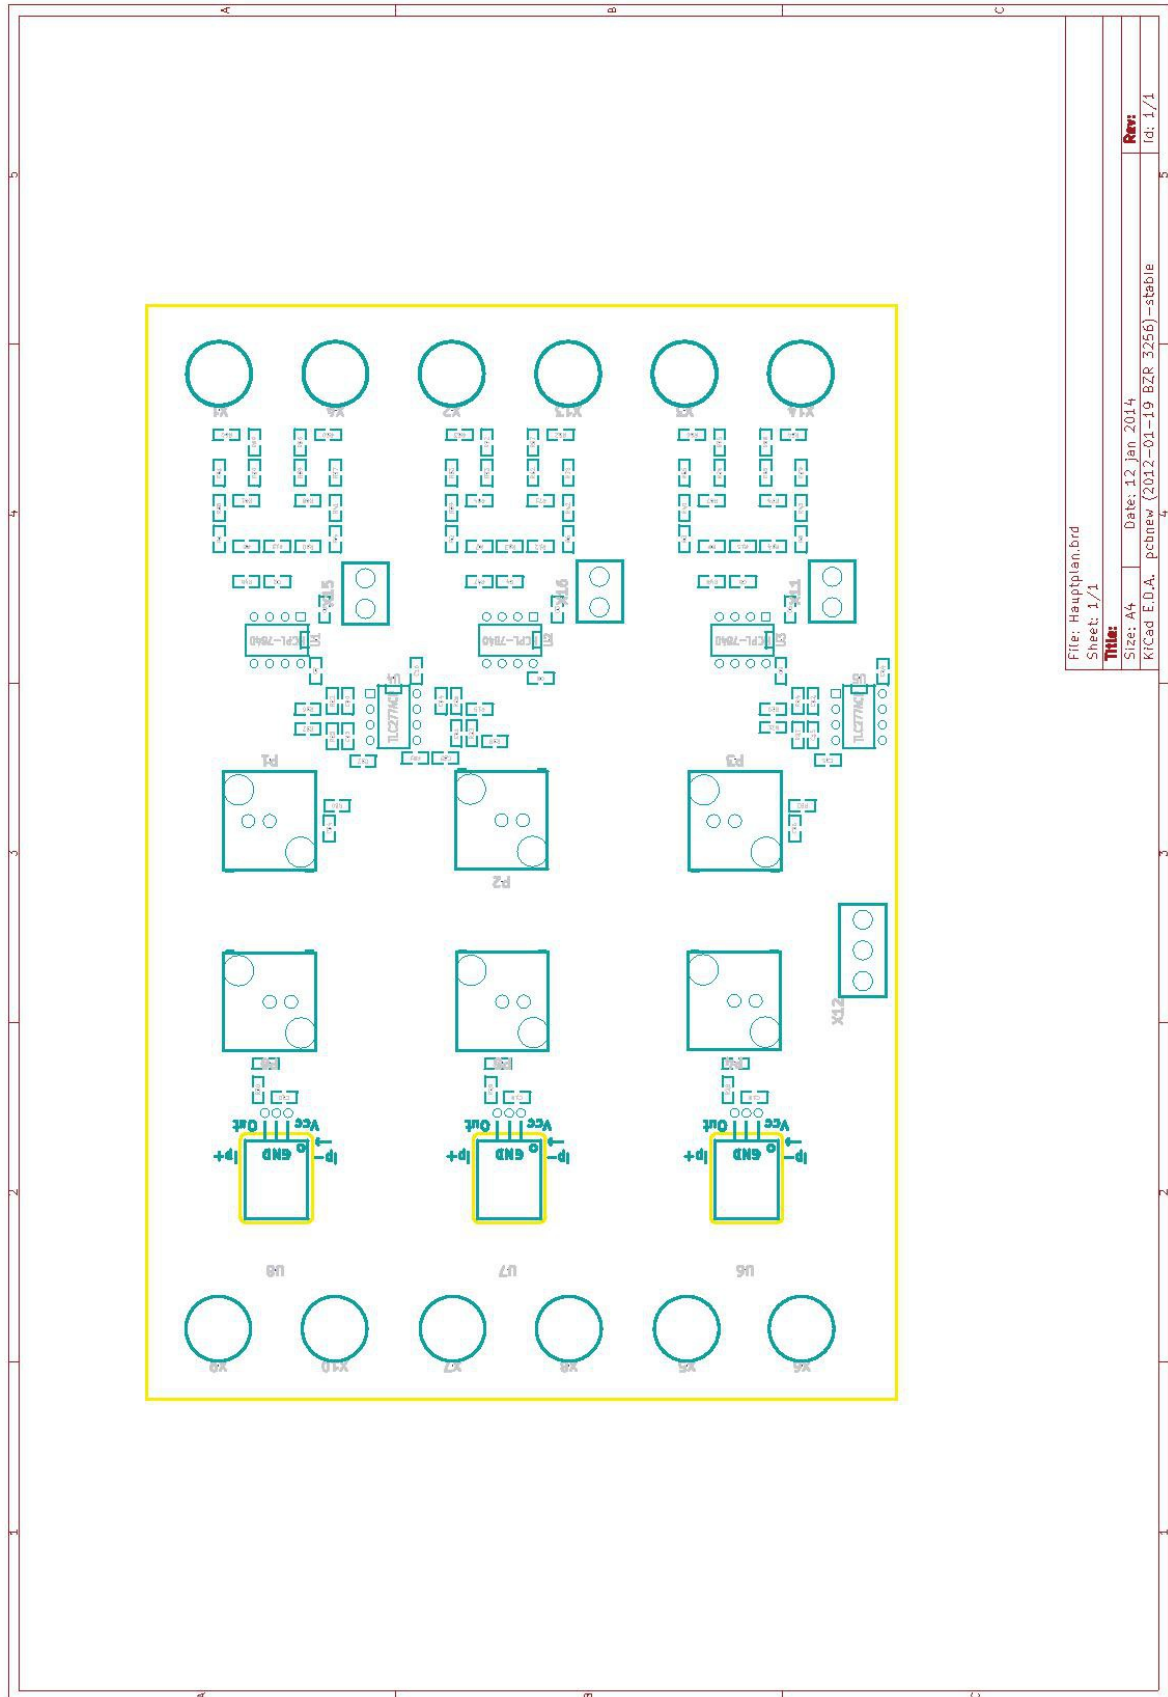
PCB-Layout Siebdruck der Gruppierungen 1 und 2
